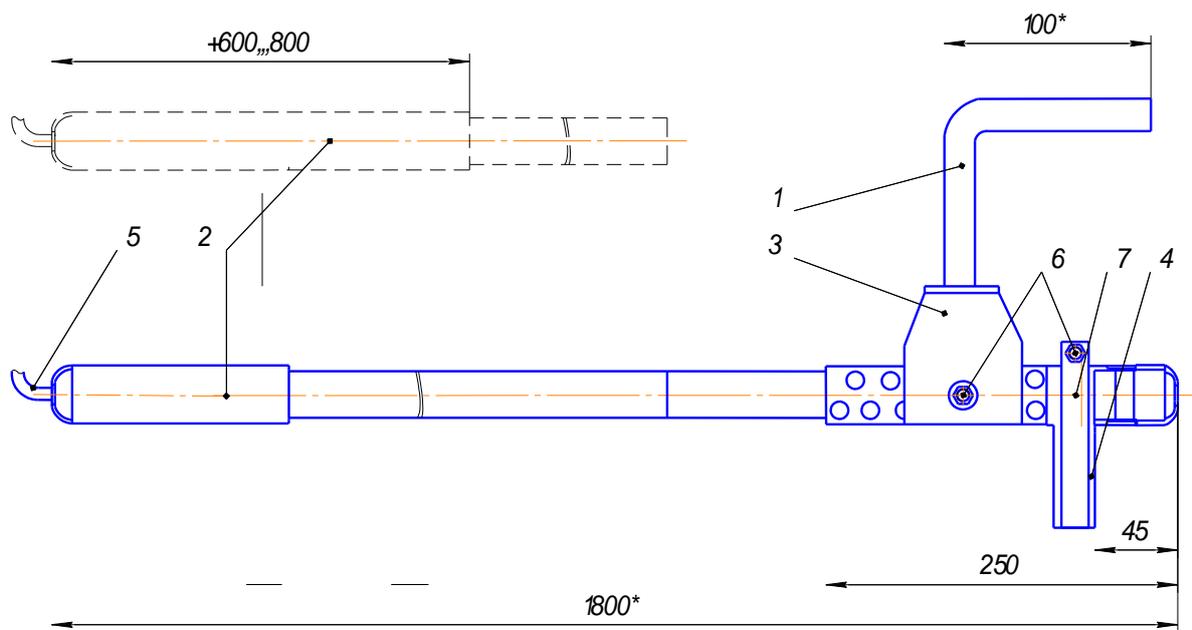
Общий вид пробозаборника дымомера с удлиненной штангой
